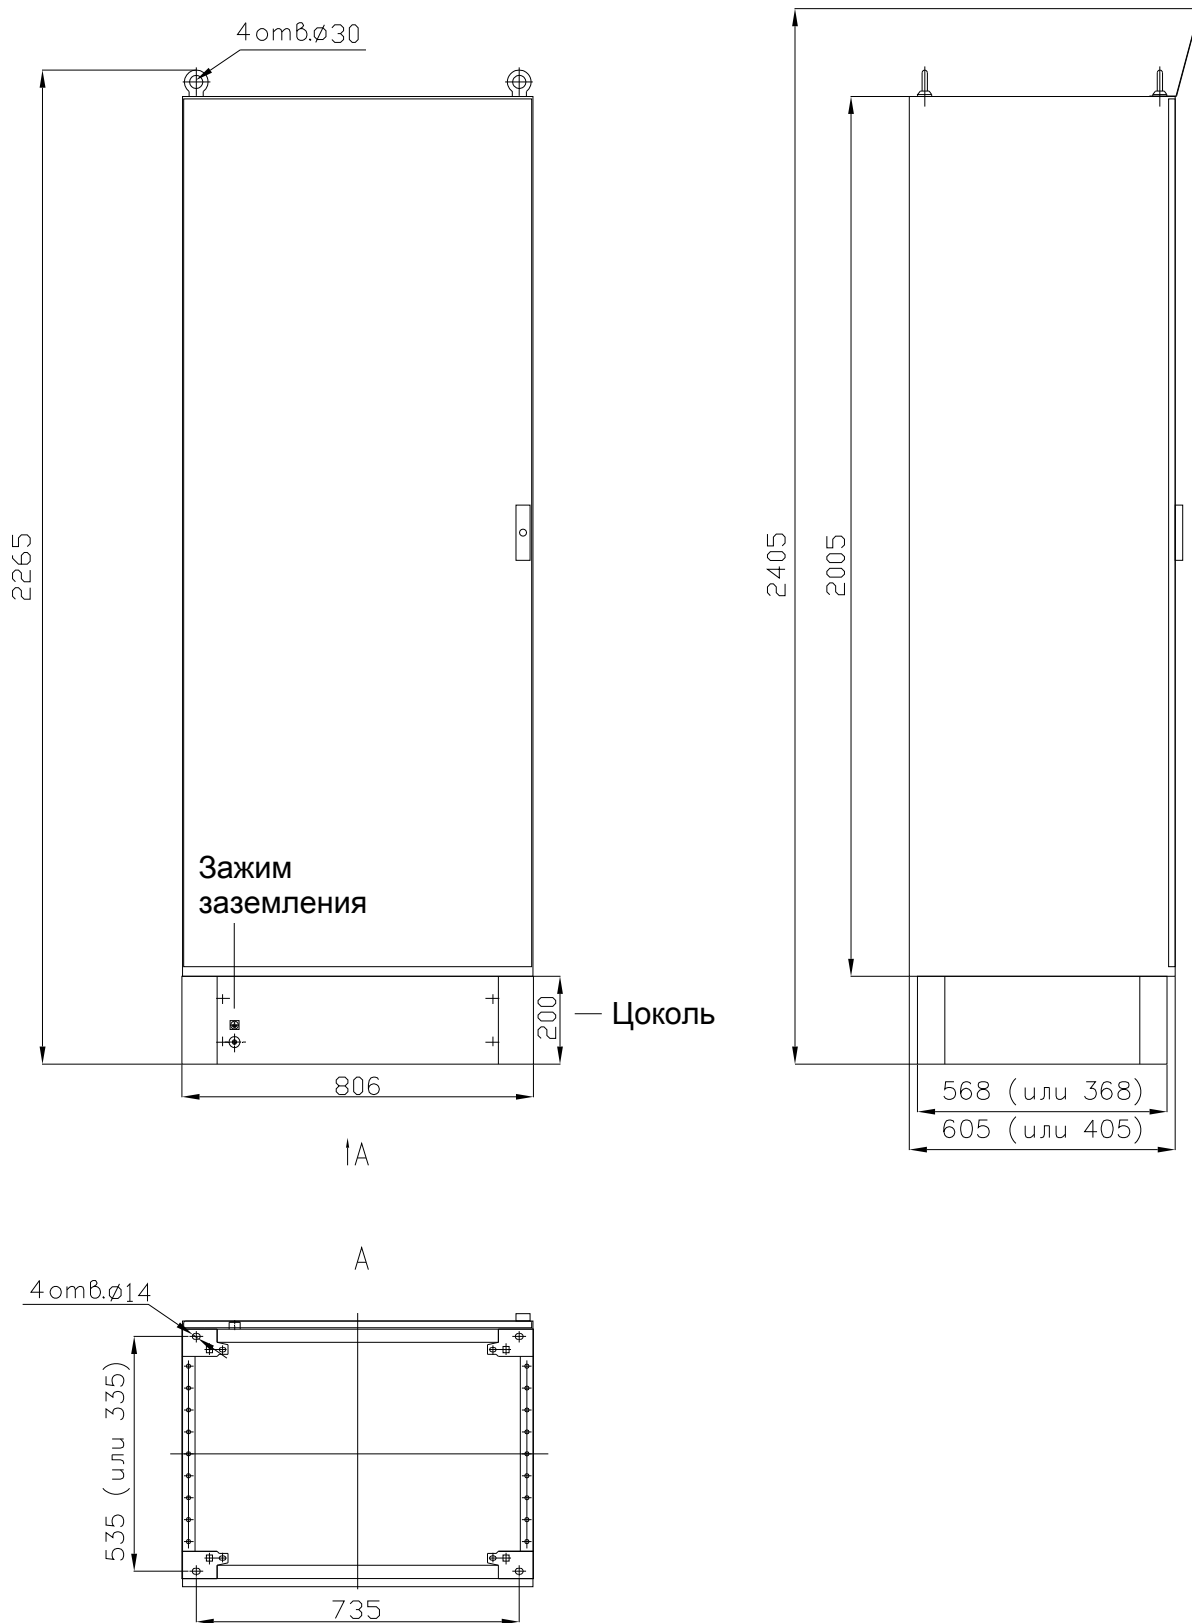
Пример внешнего вида шкафа в корпусе КС с габаритными и установочными размерами (козырёк не показан)
